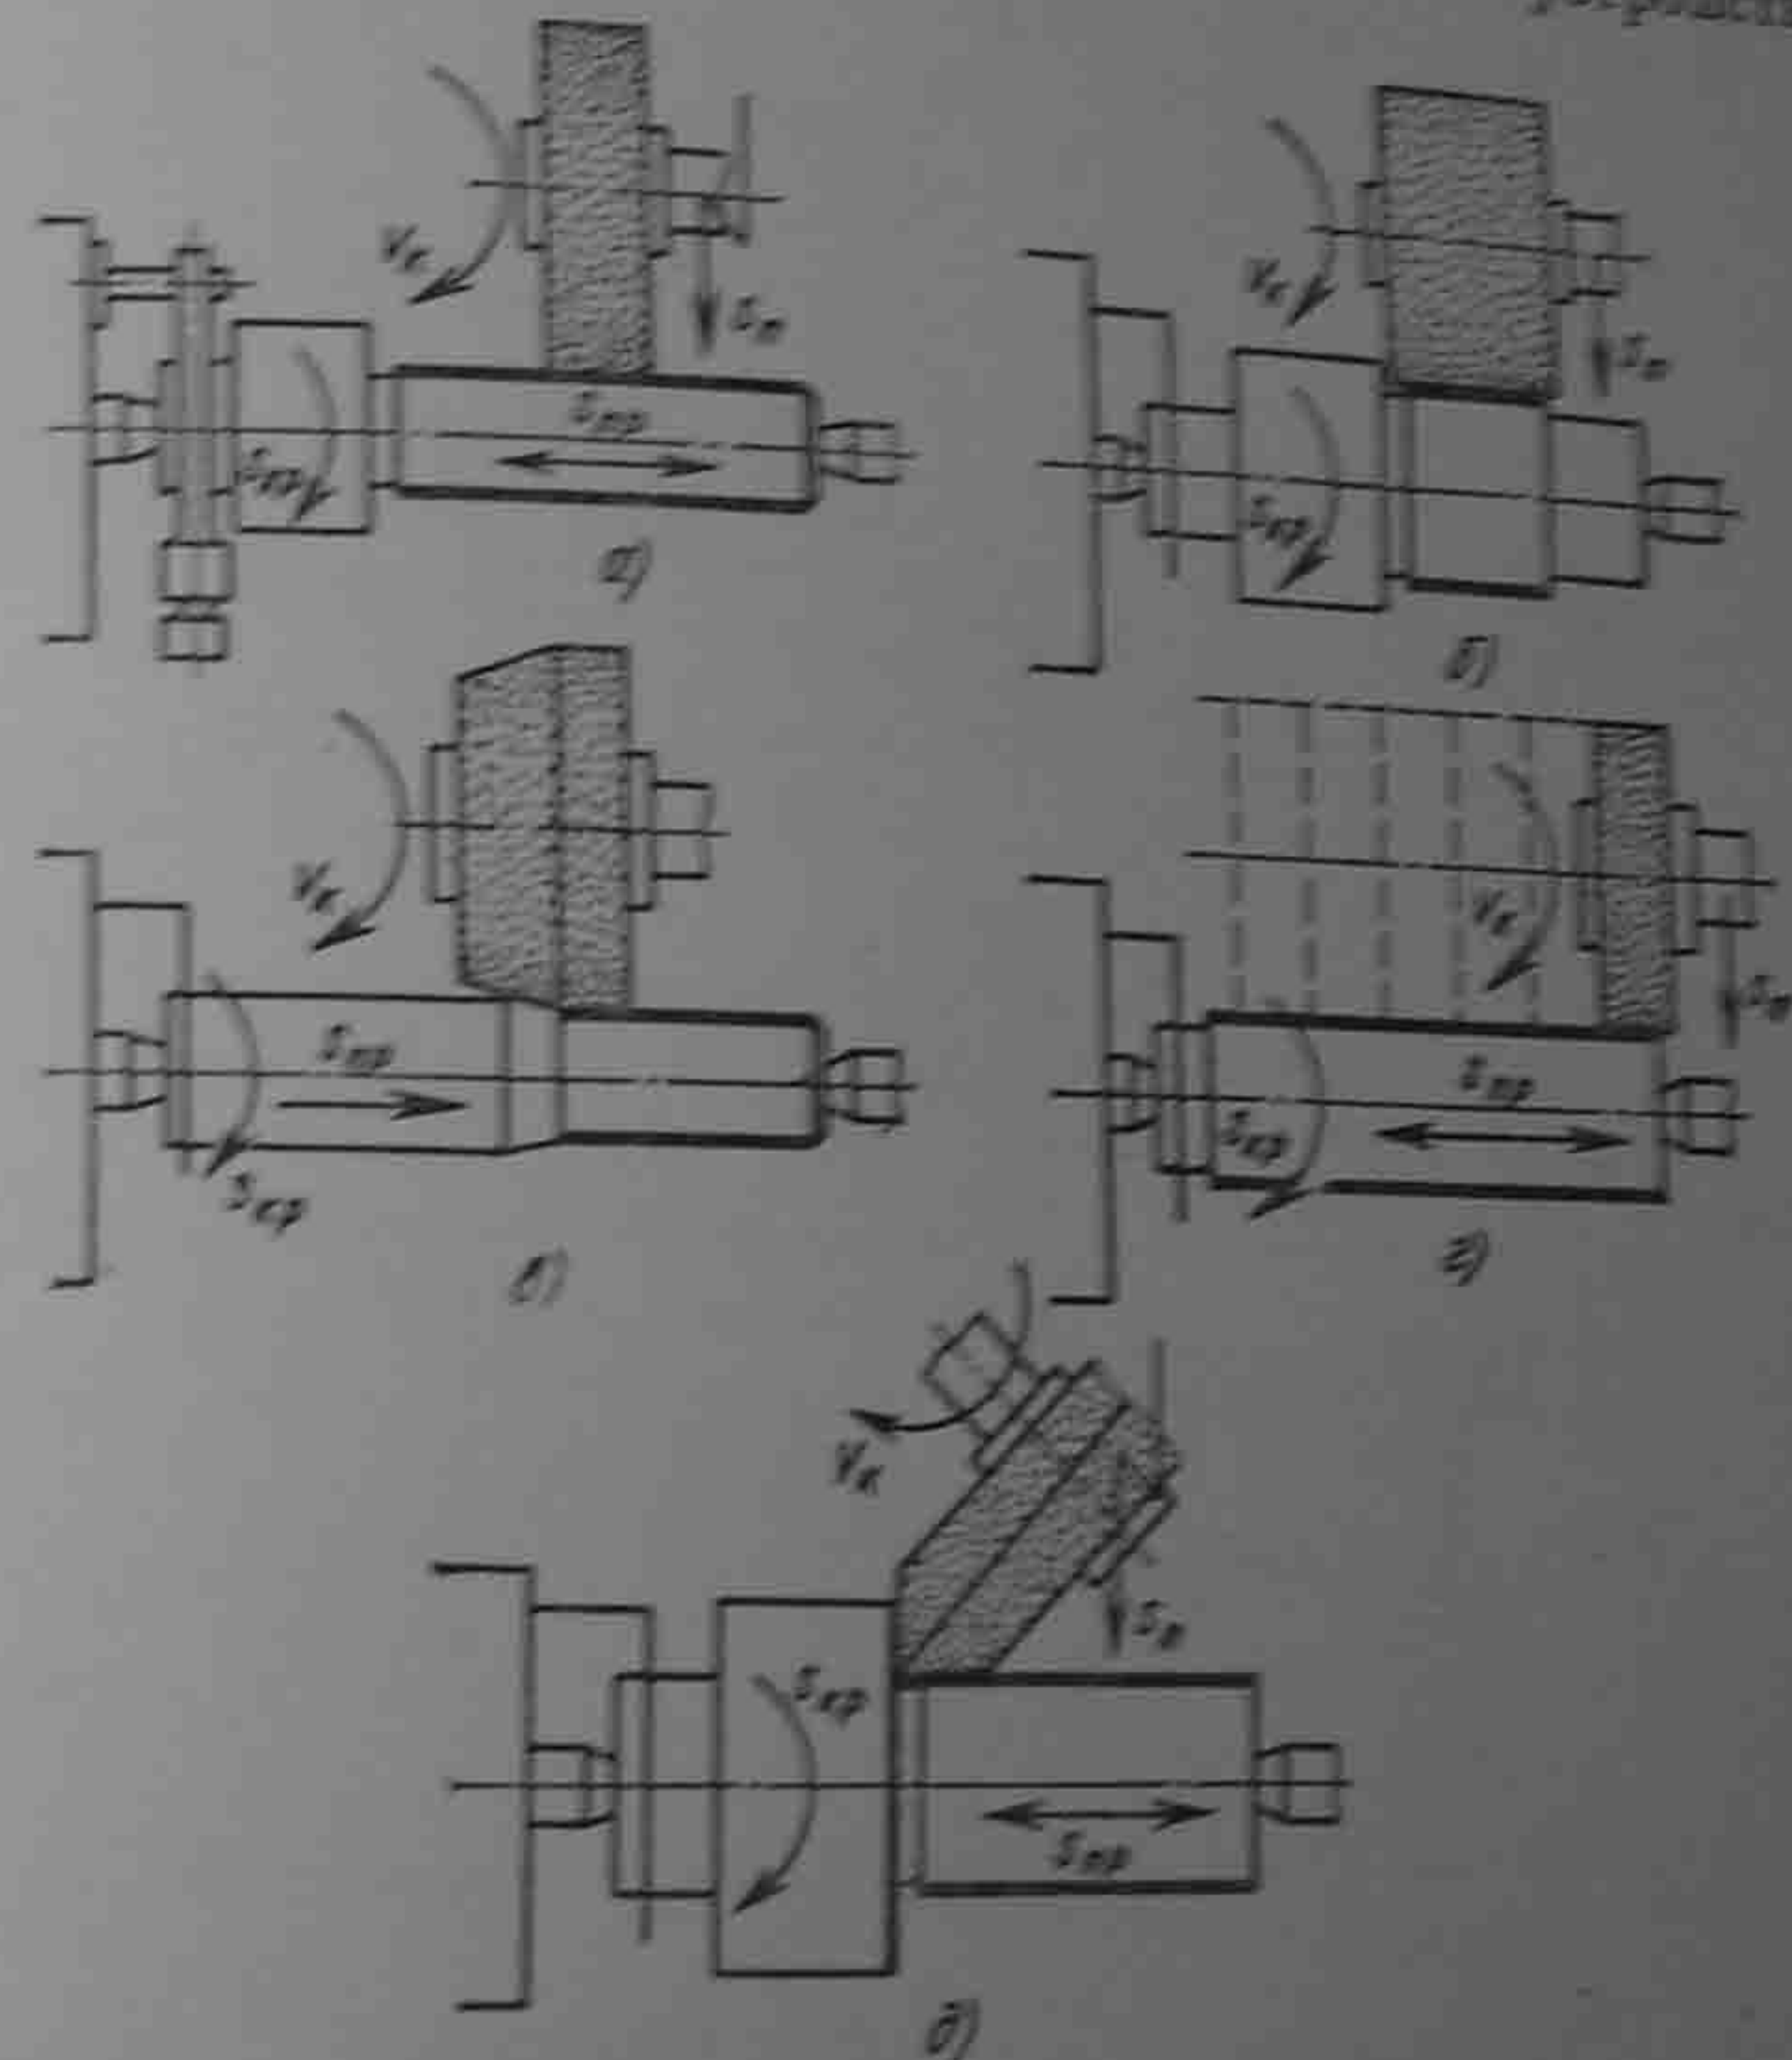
Схемы обработки заготовок на круглошлифовальных станках
